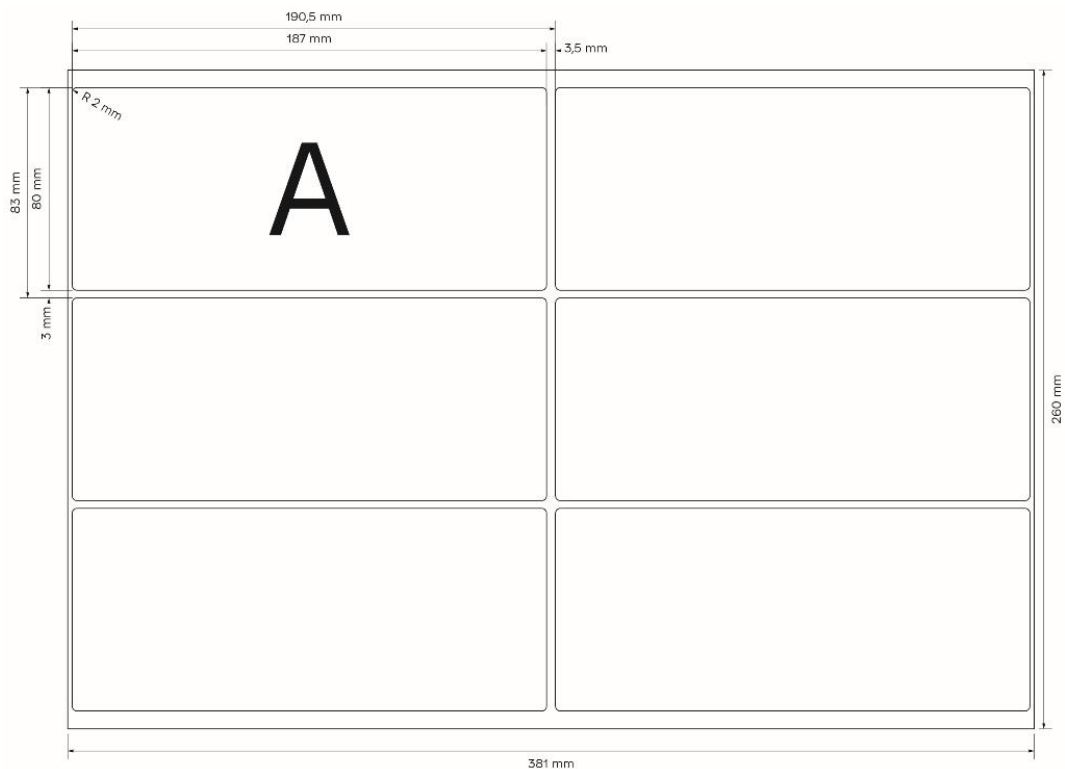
Схема розгортки та конструкція штанцформи
